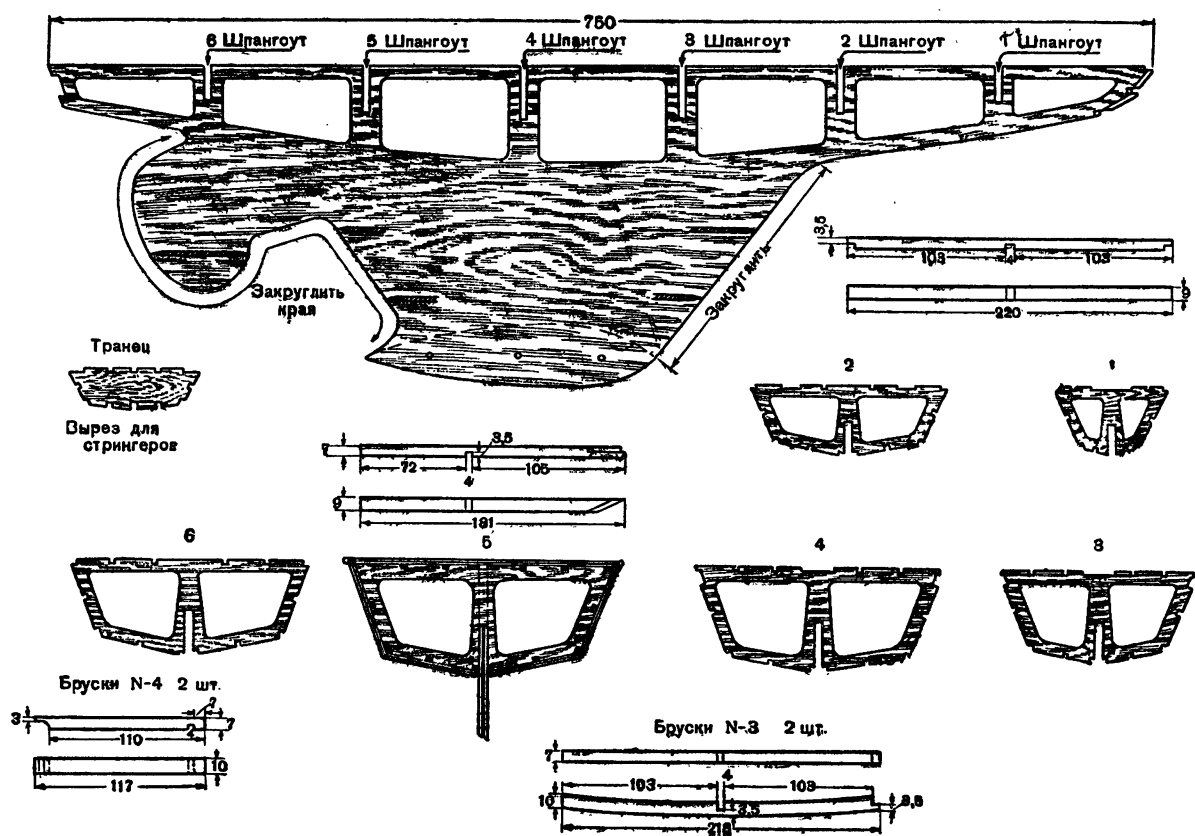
Конструктивный чертеж модели яхты класса «П».
